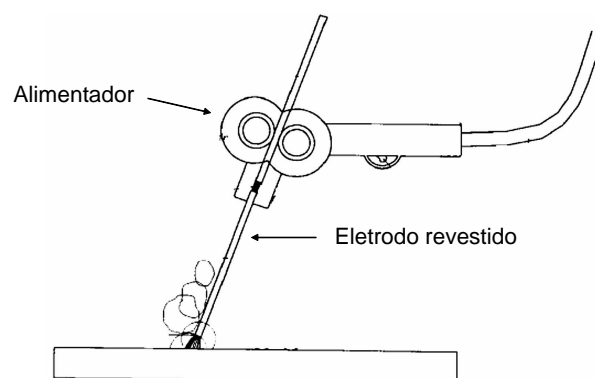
Ferramenta com alimentação mecanizada de eletrodo revestido utilizada para soldagem subaquática [Kang, 1996].
